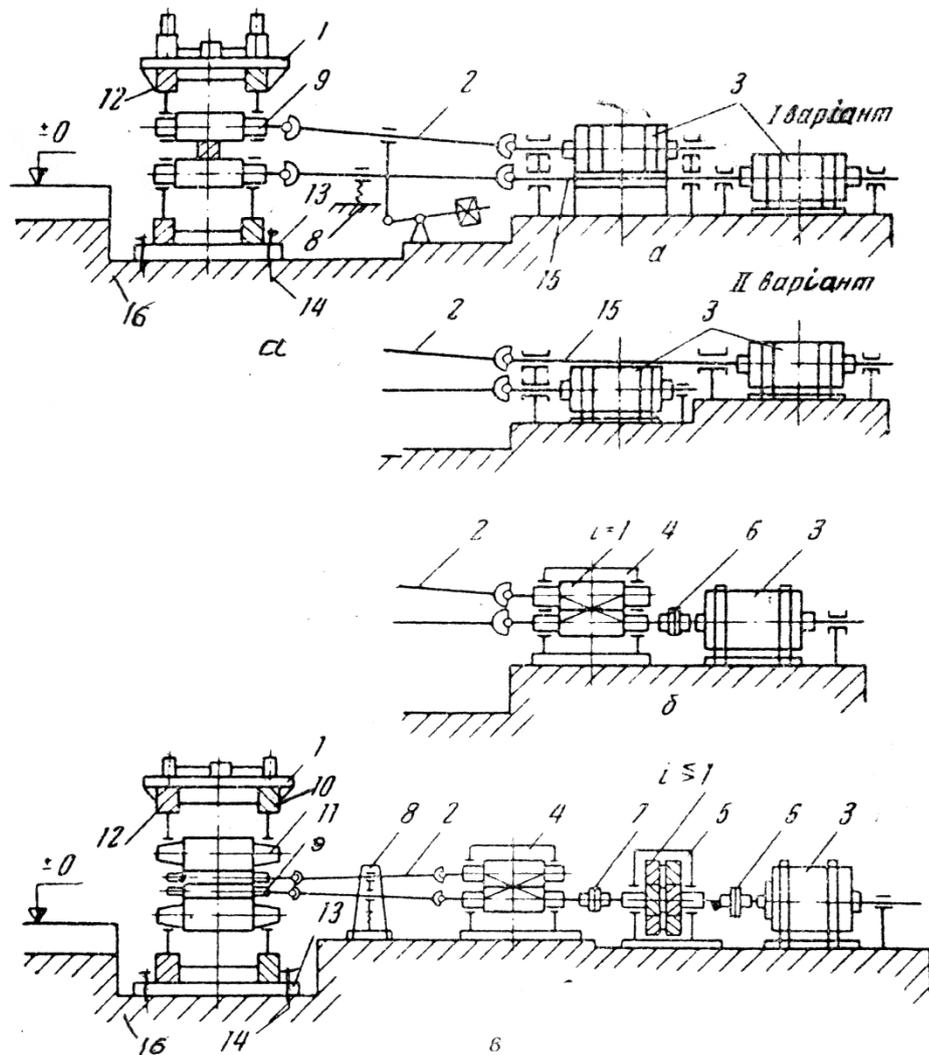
Типи головних ліній: *a* – індивідуальний привод валків; *б* – привод через шестерінчасту кліть; *в* – привод через редуктор і шестерінчасту кліть; 1 – робоча кліть; 2 – шпинделі; 3 – електродвигуни; 4 – шестерінчаста кліть; 5 – редуктор; 6,7 – муфти; 8 – врівноваження шпинделів; 9 – робочі валки; 10 і 12 – станини; 11 – опорні валки; 13 – плитовими; 14 – анкерні болти; 15 – проміжні валі; 16 – фундамент.
